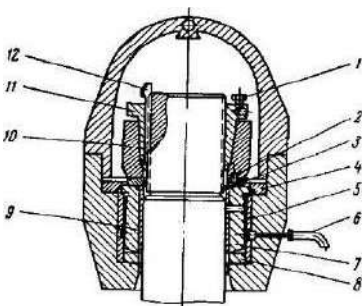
Подвес подвижного конуса дробилки ККД – 1500/180:
